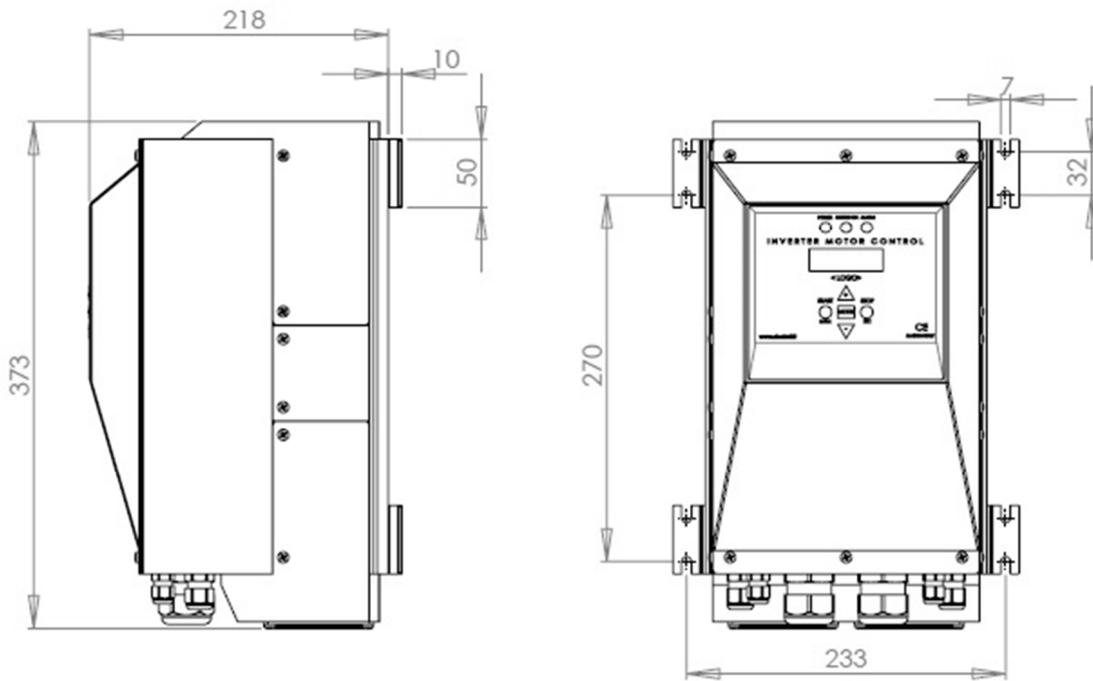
Dimensions de fixation pour ITTP (D)11W et ITTP (D)15W
